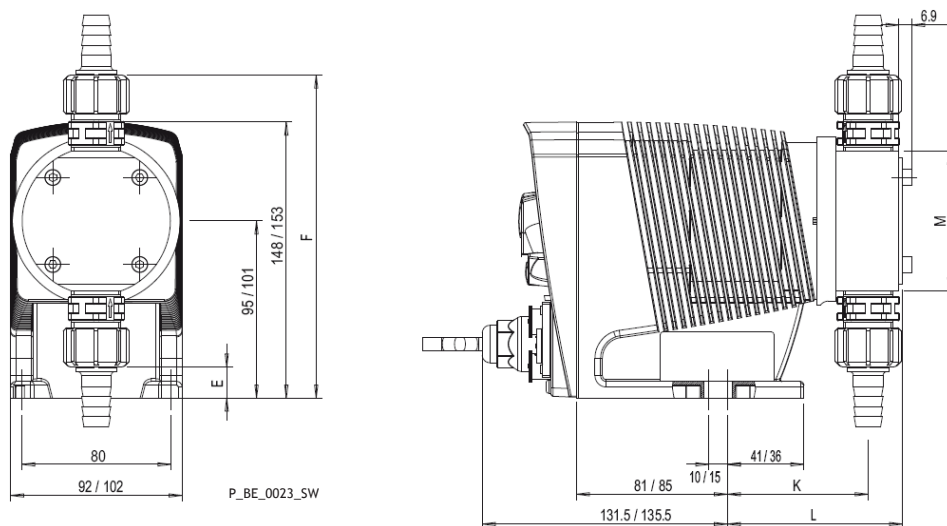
Размерный чертеж Beta® BT4b/BT5b, Материал конструкции PV для высоковязких сред – размеры в мм
